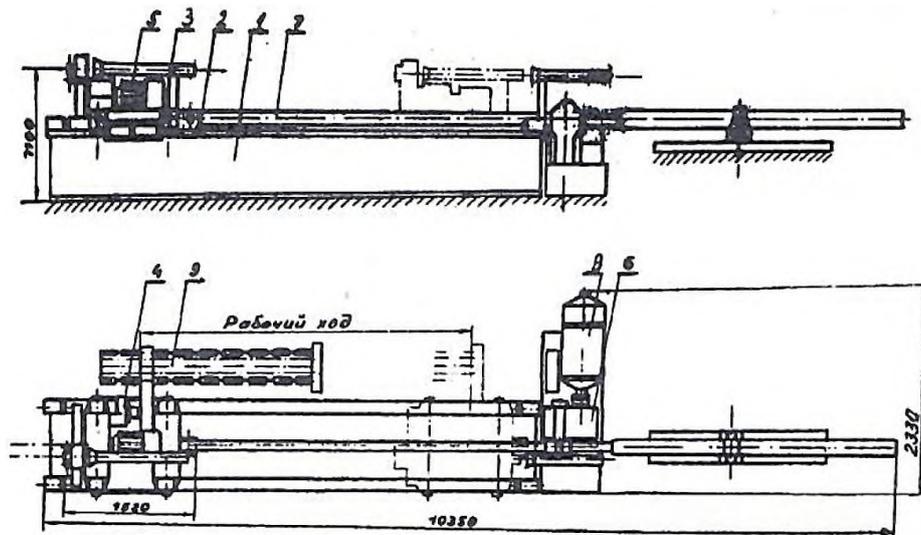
Конструктивная схема летучей реверсивной пилы [4]
